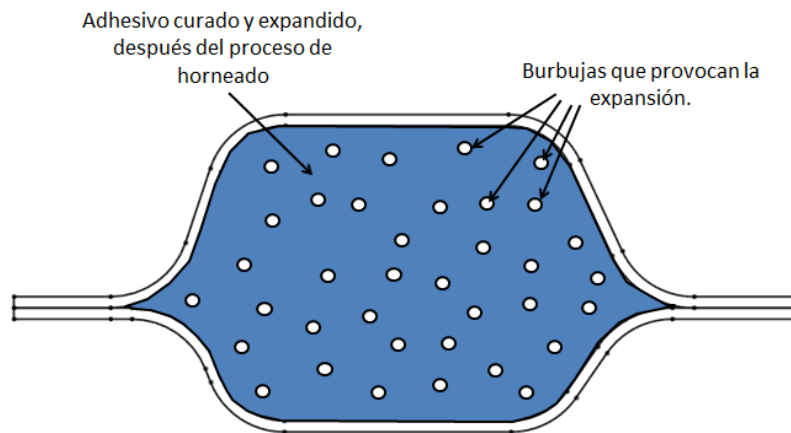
Ilustración de planilla de adhesivos estructurales.
